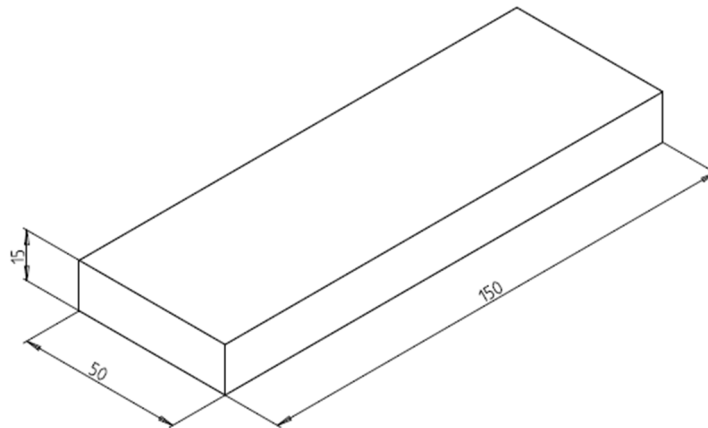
Maßzeichnung für die Auftragsschweißungen auf S235 JR
